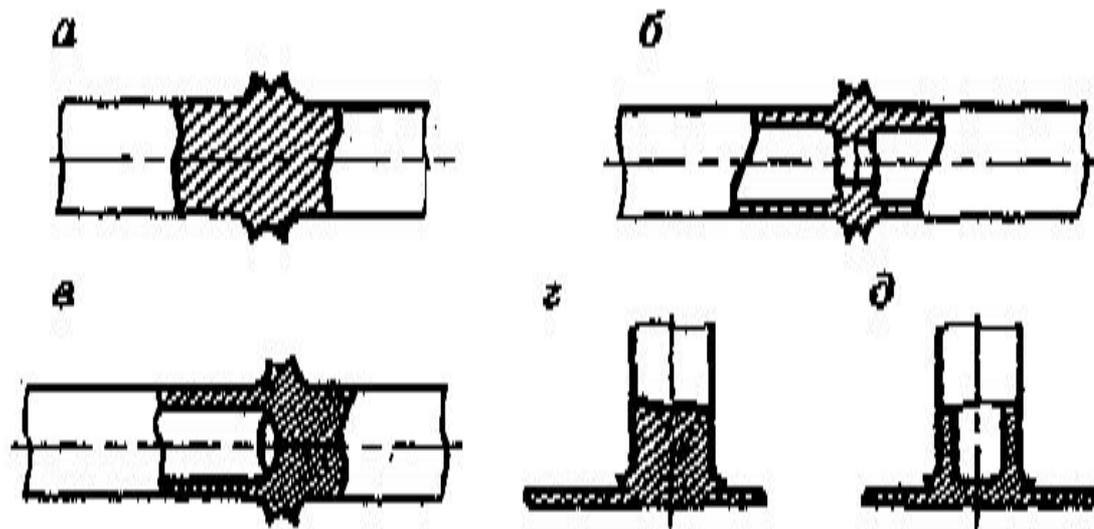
Типы соединений, выполняемых с помощью сварки трением:
